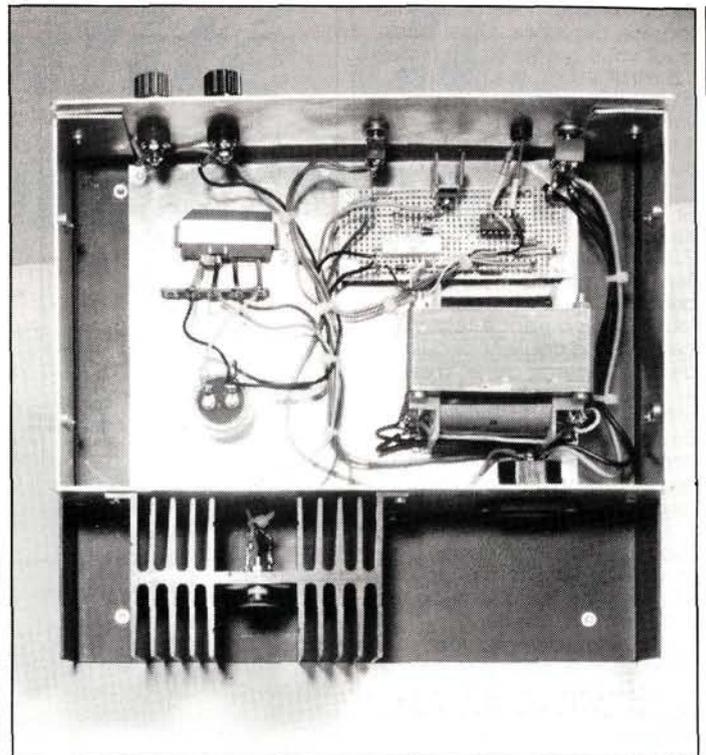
L'un de nos prototypes sans son capot. Le câblage doit être soigné : disposition, section, soudure, isolation.
